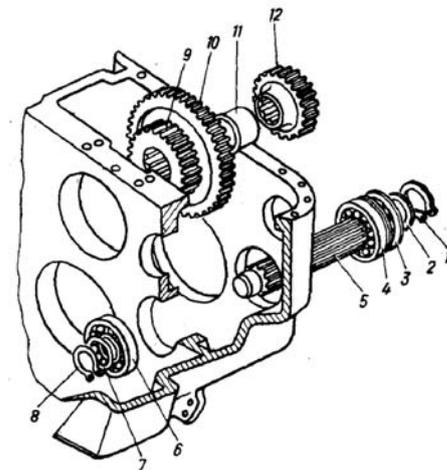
Установка ходоуменьшителя: 1, 2, 3, 7, 8 — кольцо; 4, 6 — подшипник; 5 — вал; 9, 10, 12 — колесо зубчатое; 11 — втулка
